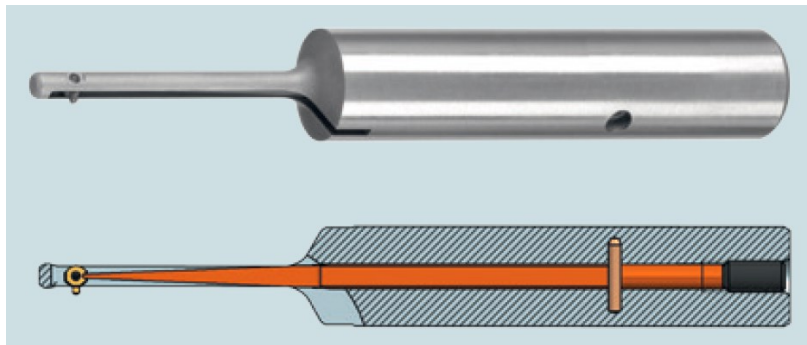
Prinzipieller Aufbau des Heule COFA C2 Werkzeugs für Bohrungen.¹⁴⁶
